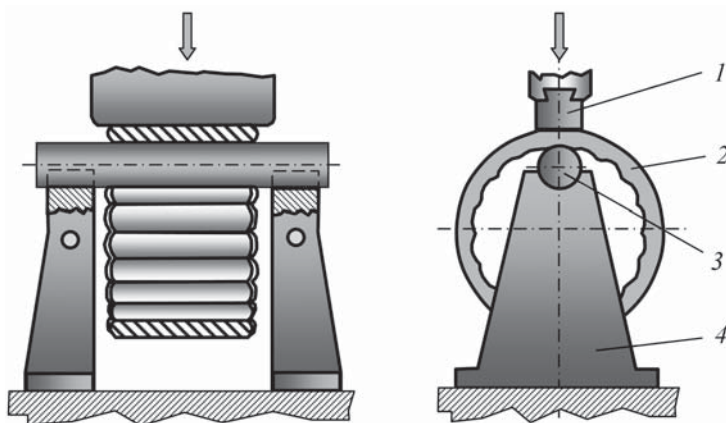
Схема раскатки кольцевой заготовки на оправке:
